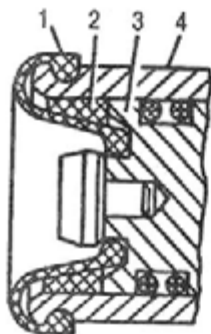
Установка пенополиуретанового кольца в колесные цилиндры:
